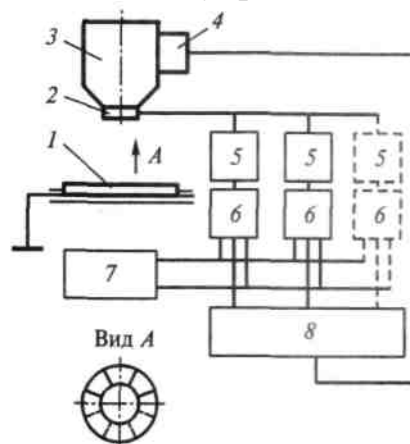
11 Схема пристрою контролю технологічного зазору сопла лазерної головки
